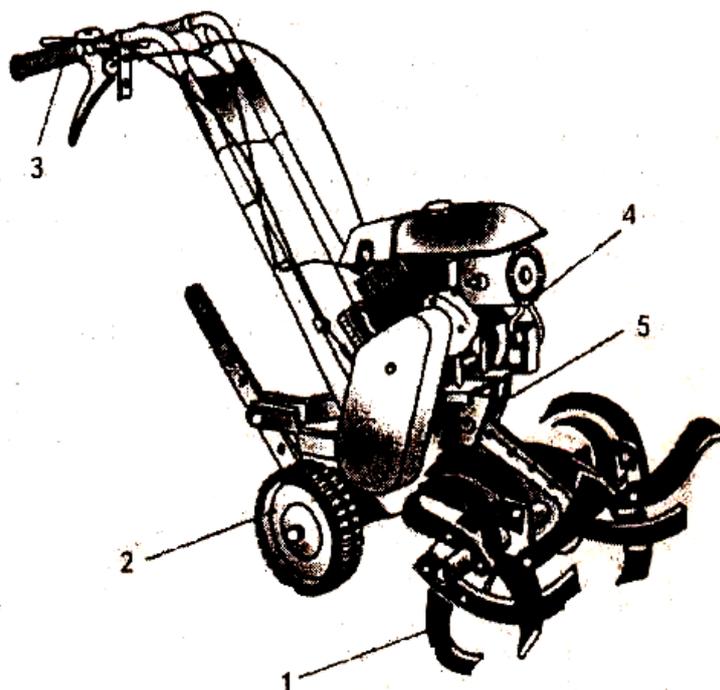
Мотофреза мк-1 «крот»: 1 – фреза; 2 – ходовые колеса; 3 – рукоятка управления; 4 – двигатель; 5 – рама
